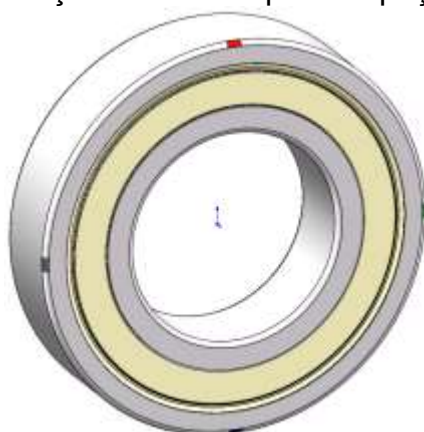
Detalhe de furo para inspeção do rolamento.
